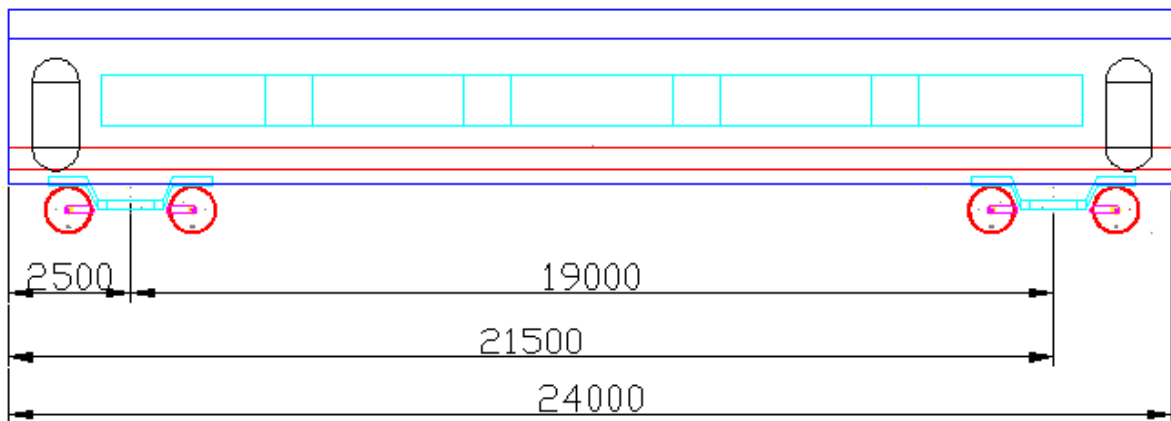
Disposición acotada de los bogies medido en milímetros.
